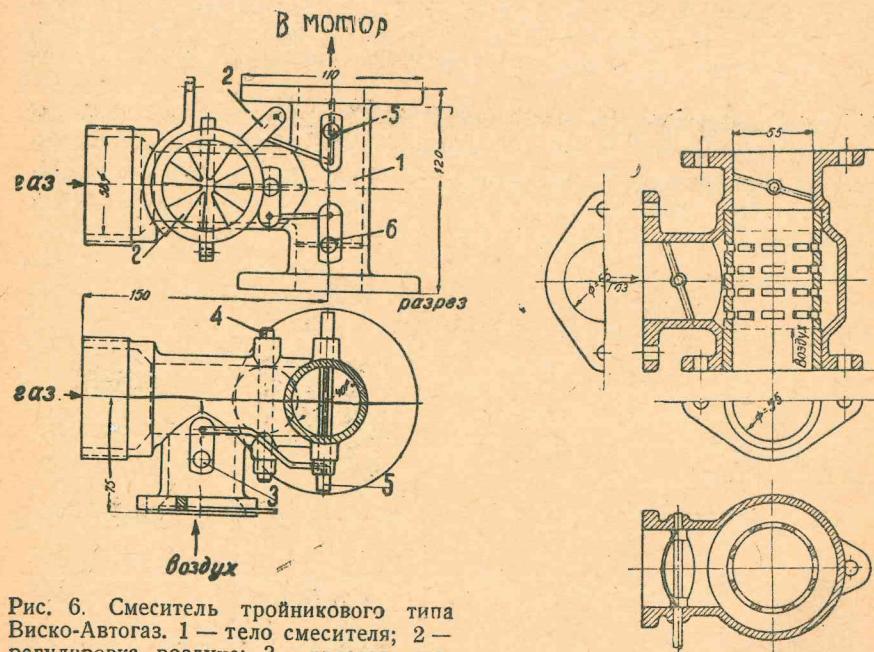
Смеситель тройникового типа Виско-Автогаз. 1 — тело смесителя; 2 — регулировка воздуха; 3 — дроссель воздуха; 4 — дроссель газовоздушной смеси; 5 — дроссель акселератора; 6 — дроссель бензина
